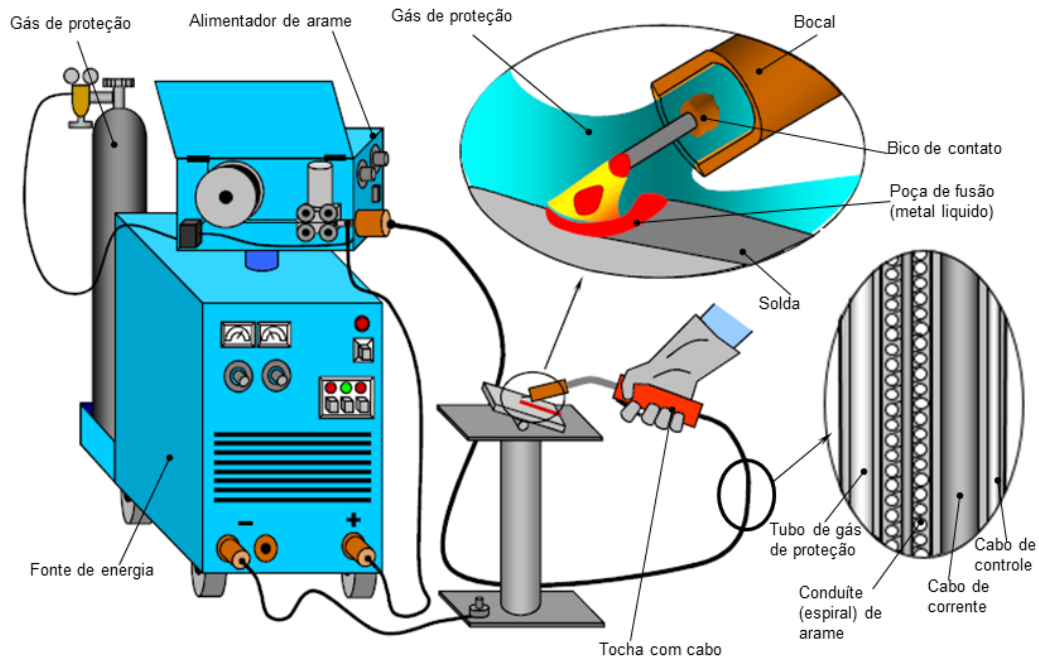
Esquema do processo de soldagem MIG/MAG. ¹⁰
